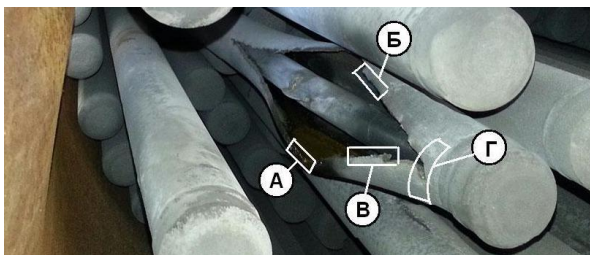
Схема отбора образцов от разрушенной трубы / Fig. 2. Sampling scheme from a broken tube
